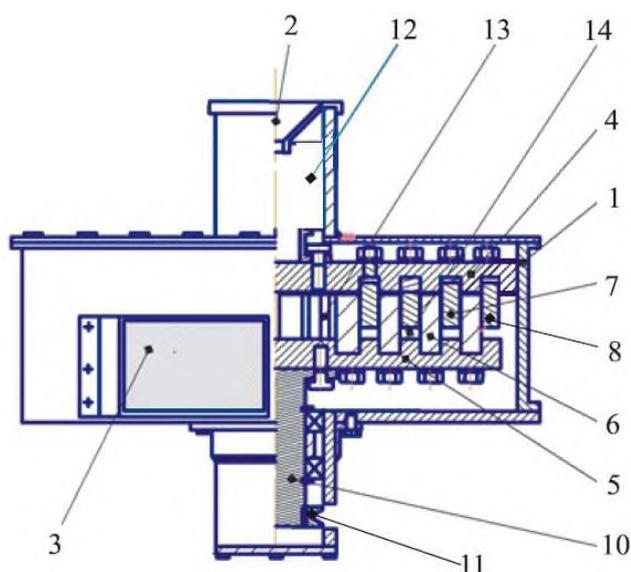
Схема измельчителя зерна центробежно-роторного типа:
